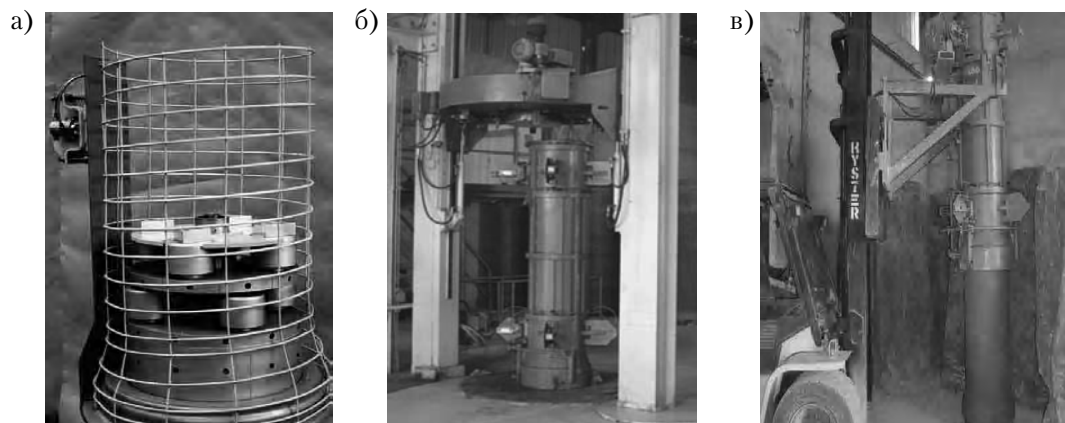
Радиальный пресс SP фирмы HESS [4]: а – формующий инструмент, арматурный каркас; б – общий вид механизма формования; в – распалубливание трубы вилочным погрузчиком.
